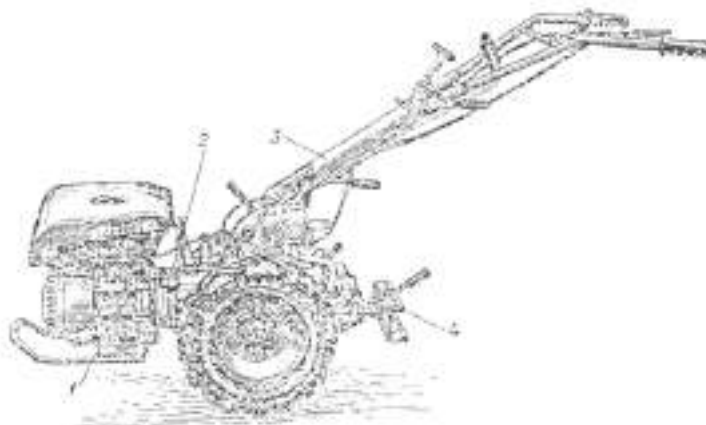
Мотоблок «Артанія»: 1 – двигун; 2 – коробка передач; 3 – штанга; 4 – прицепний засіб
